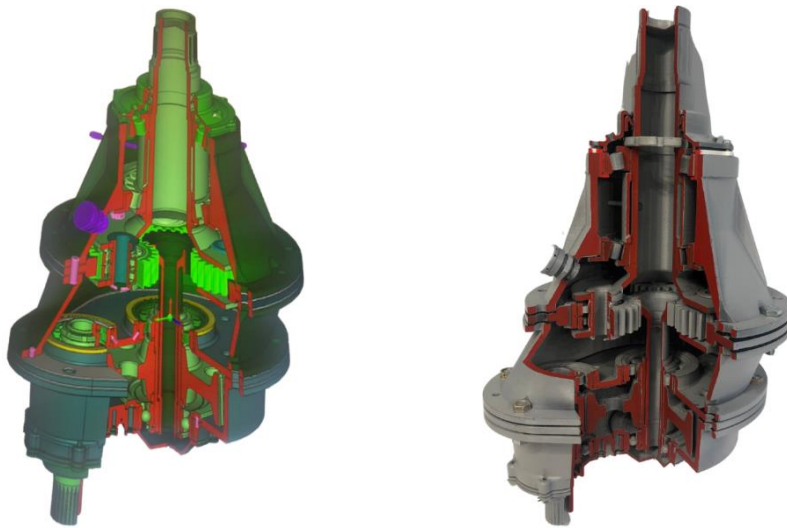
Модели деталей сборки и наглядное пособие «Конструкции вертолѐтного редуктора»
